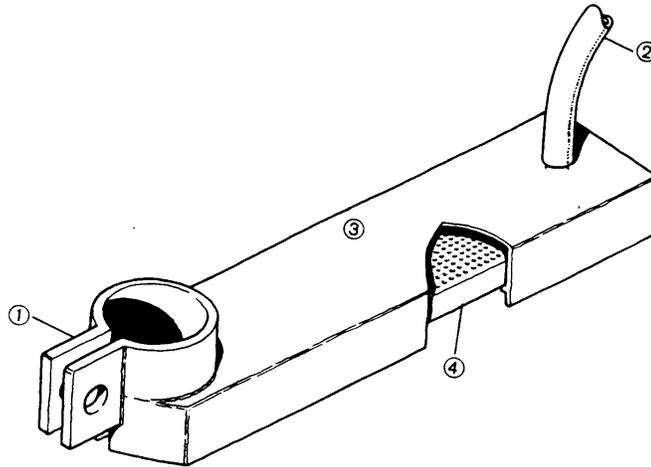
Bocal de gás alongado para soldagem mecanizada.
